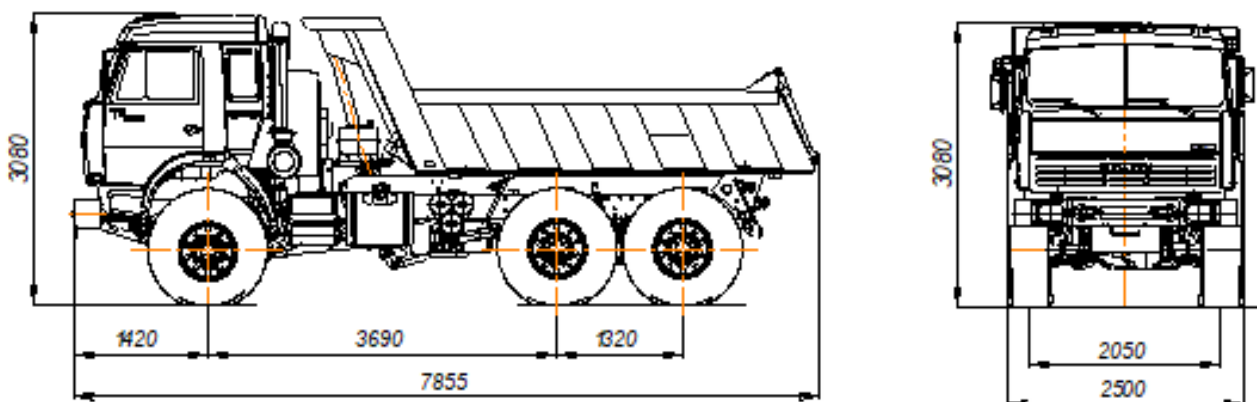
Габаритные размеры самосвала КАМАЗ 45141-011-50 [77]
